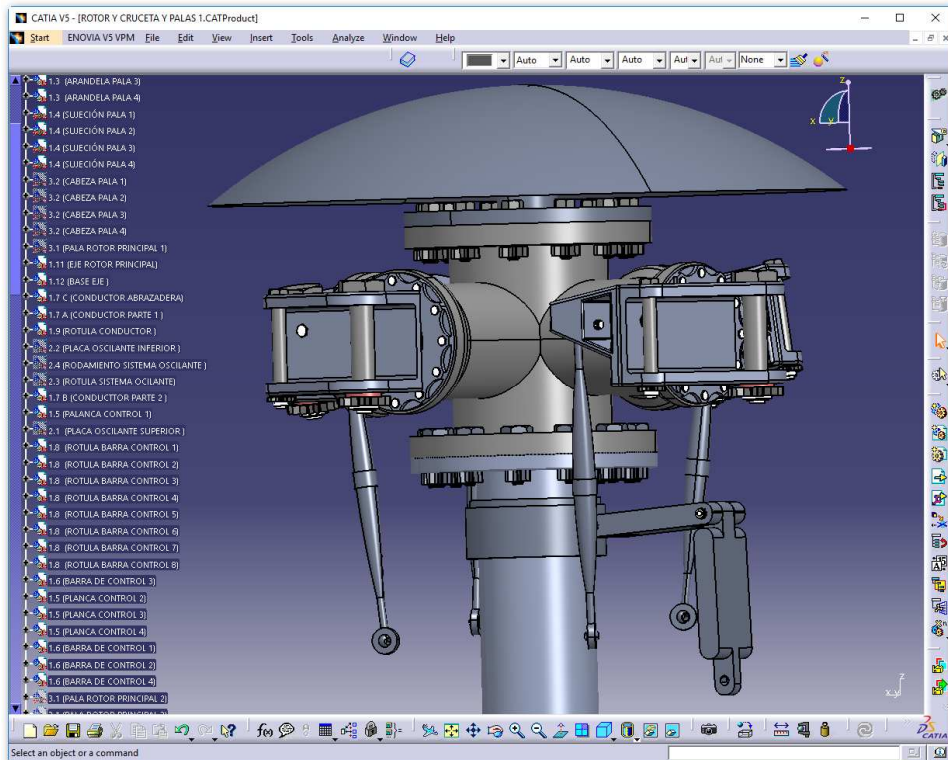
Conjunto cabeza rotor principal.
